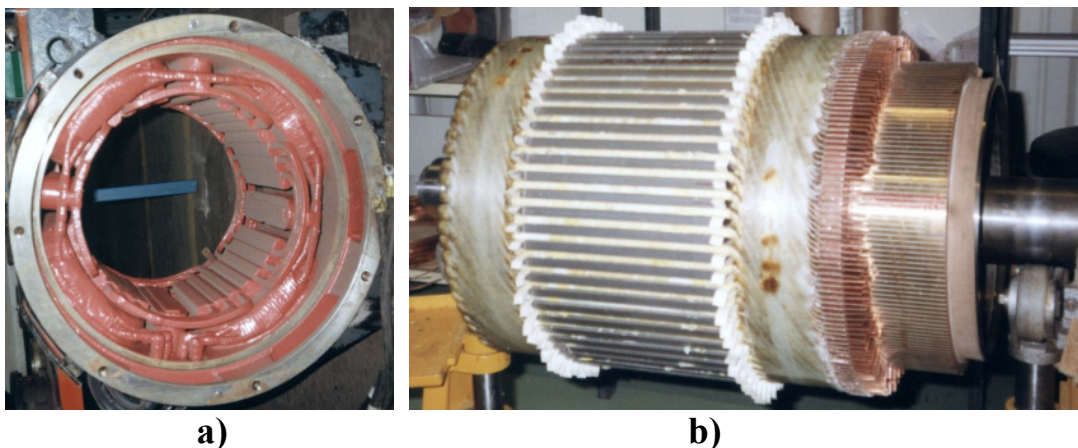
a) Estator y b) rotor de una máquina de c.c. durante su proceso de fabricación.
